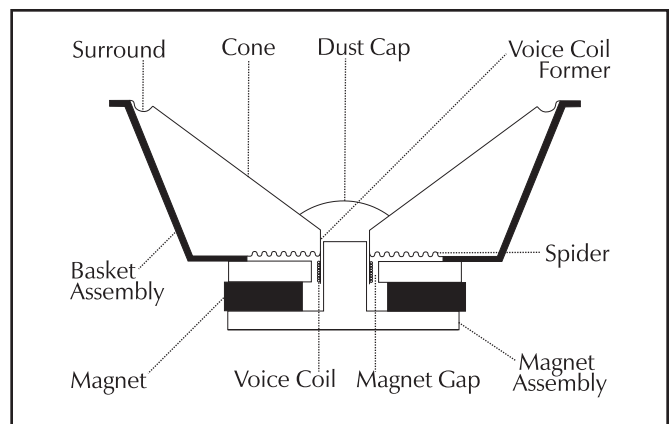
Vue en coupe d'un haut-parleur à bobine en mouvement typique. Remarquez la complexité due au grand nombre de pièces utilisées.
